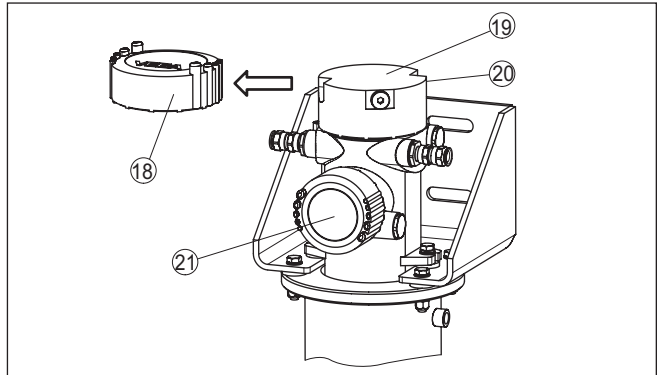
Montaje de la tapa de refrigeración de la carcasa
